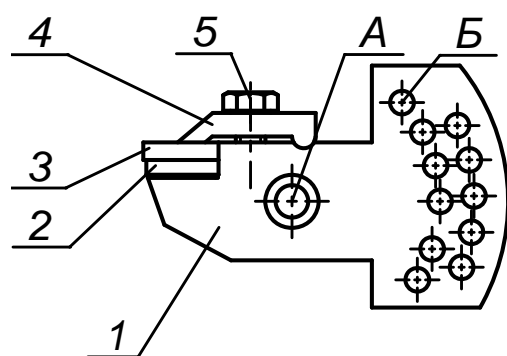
Нож с закреплением режущей пластины прихватом: 1 – державка; 2 – опорная пластина; 3 – режущая пластина; 4 – прихват; 5 – болт; А – осевое отверстие; Б – отверстия под фиксирующий болт
